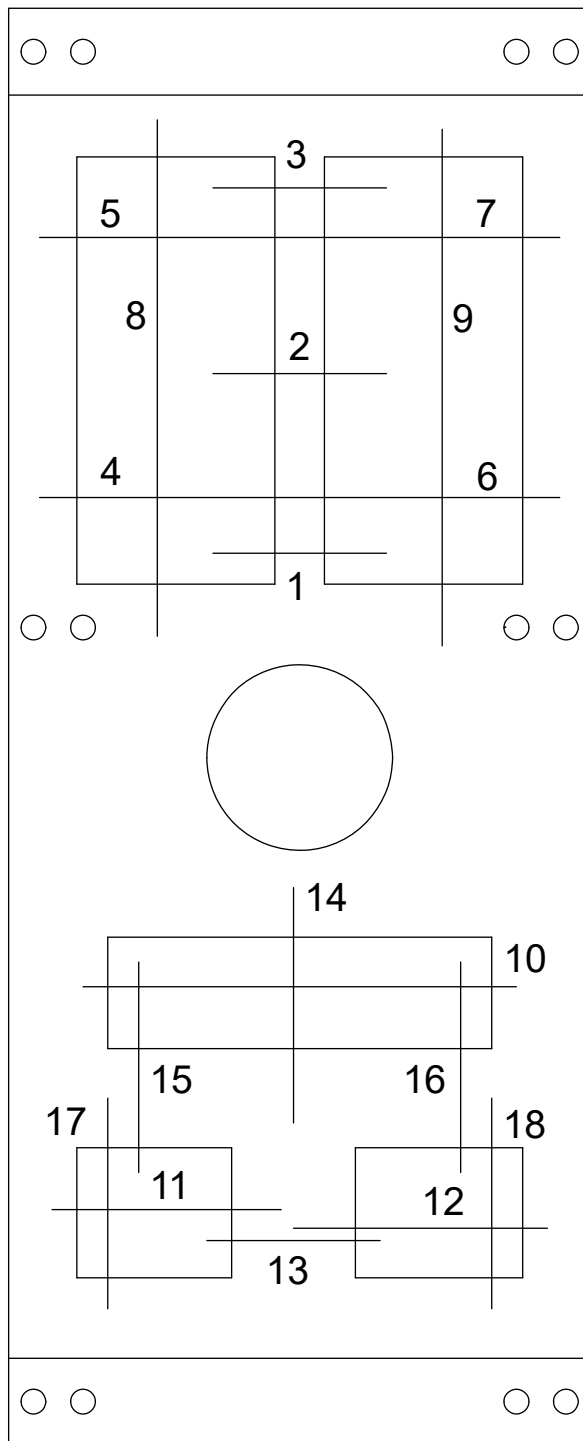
Выровняйте (горизонтируйте) монтажные площадки привода
